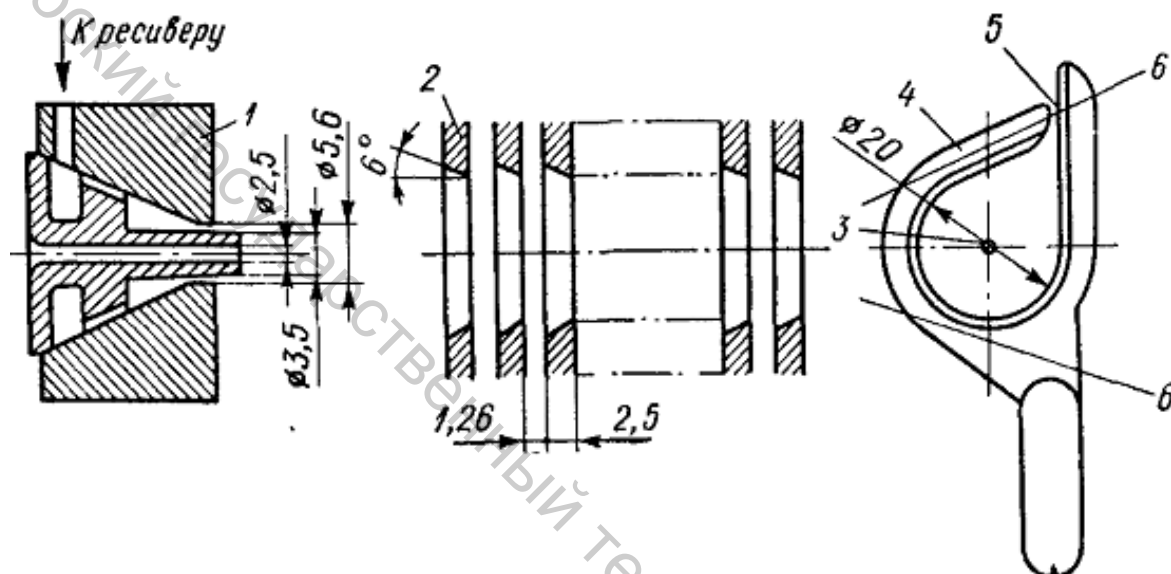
Схема пневматической системы ткацкого станка П-105
